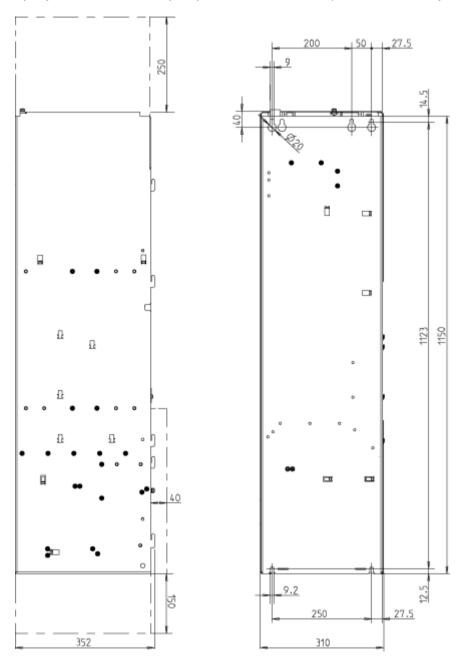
Габаритный чертеж модуля питания Basic, типоразмер FB. вид сбоку, вид сзади
